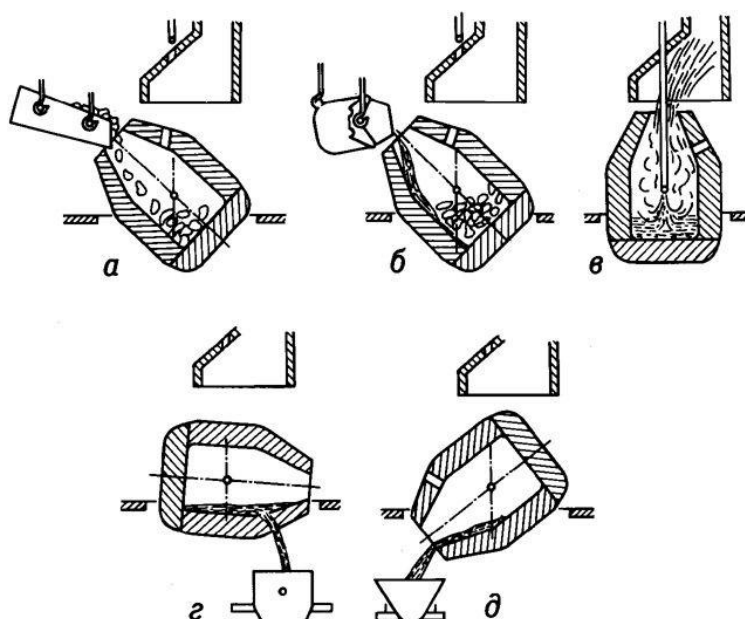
Схема получения стали в кислородном конвертере: а — загрузка металлолома; б — заливка чугуна, в - продувка: г — выпуск стали: д — слив шлака
